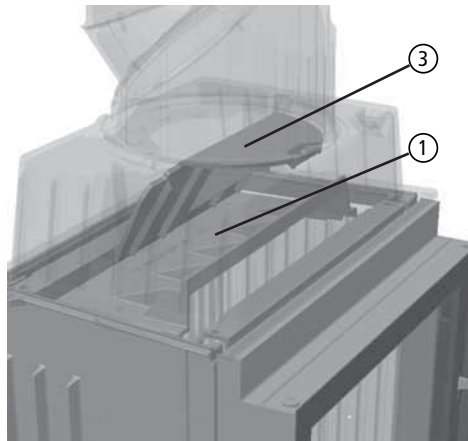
Guss-Umlenkung und Guss-Prallplatte im VIDA 68
